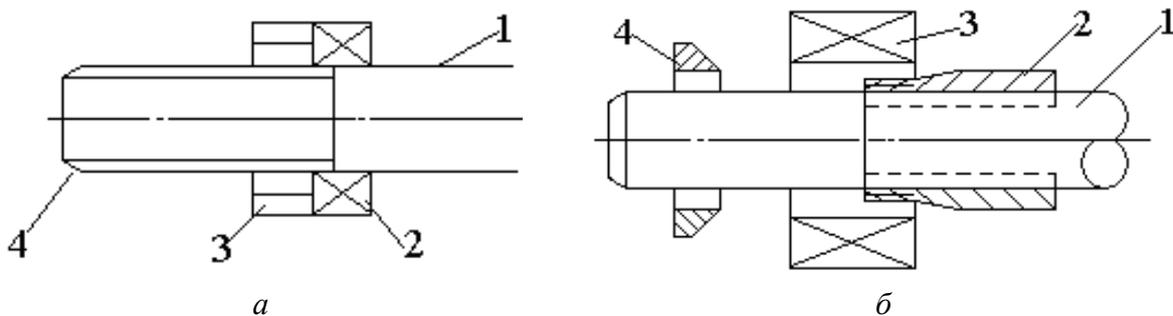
Сборка подшипника качения: а – с помощью резьбы: 1 – вал; 2 – подшипник; 3 – гайка; 4 – резьба; б – с помощью втулки: 1 – вал; 2 – втулка разрезная; 3 – подшипник; 4 – гайка
